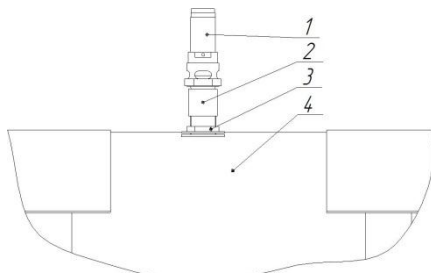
1 – Клапан предохранительный; 2 – Муфта типа В-В; 3 – Отвод воздушный для установки предохранительного клапана ; 4 – Понтон пневматический судоподъемный
